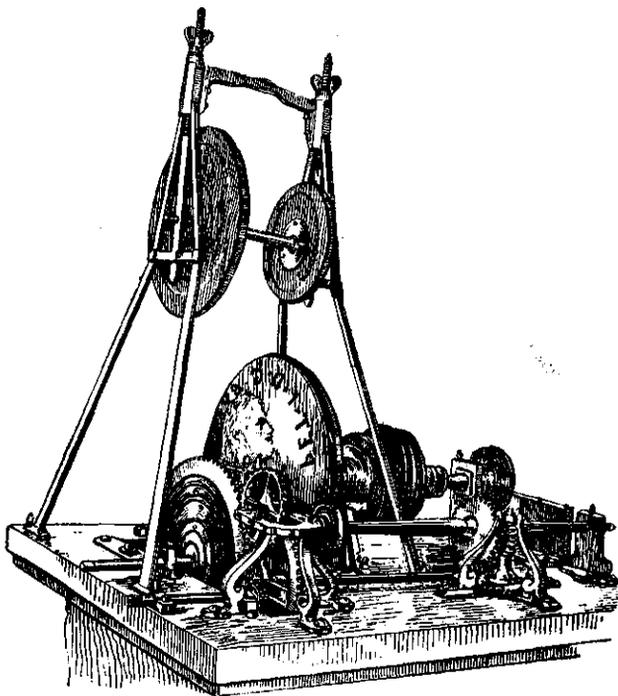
Узел механизма привода и передачи движения подачи к супортам в медальерном токарно-копировальном станке Зингера.
